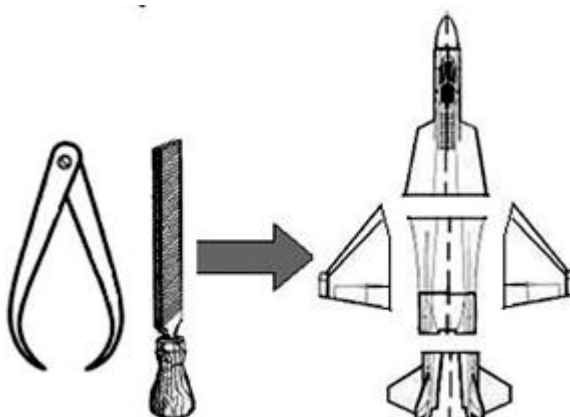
Виготовлення основних деталей виробу за своїми розмірами, обраними самостійно інструментами, матеріалами.
